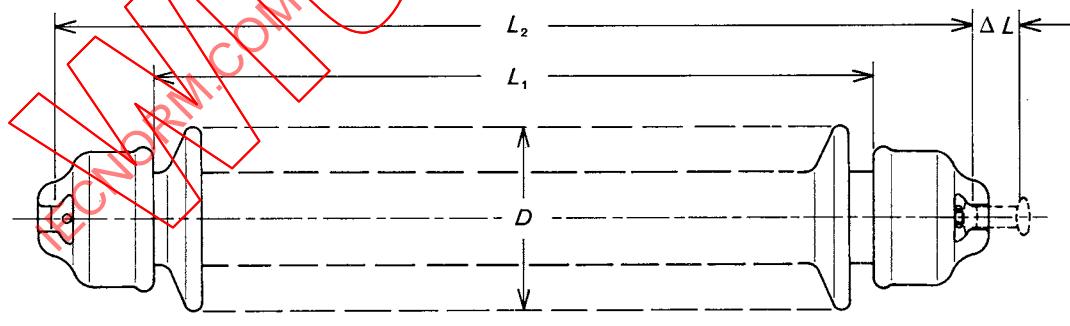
Elément de chaîne avec armatures externes et assemblage à rotule et logement de rotule,
